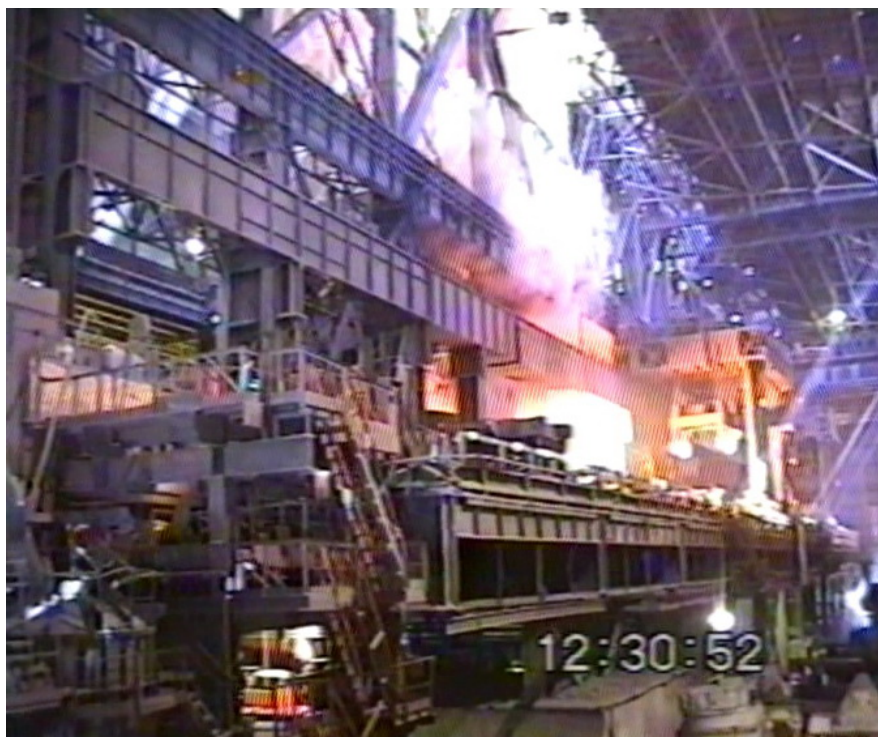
Общий вид опытной установки СЭР на переднем плане заливочного пролета конвертерного цеха
